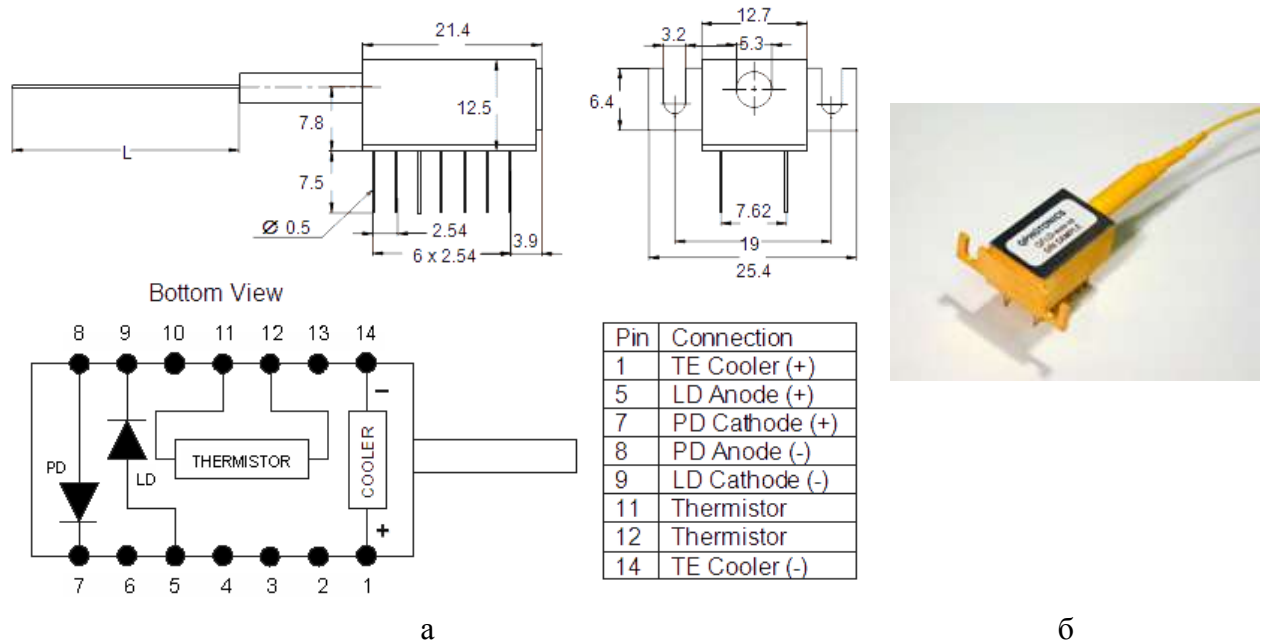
Габаритный чертеж и принципиальная схема передающего модуля (а) и его внешний вид (б)
